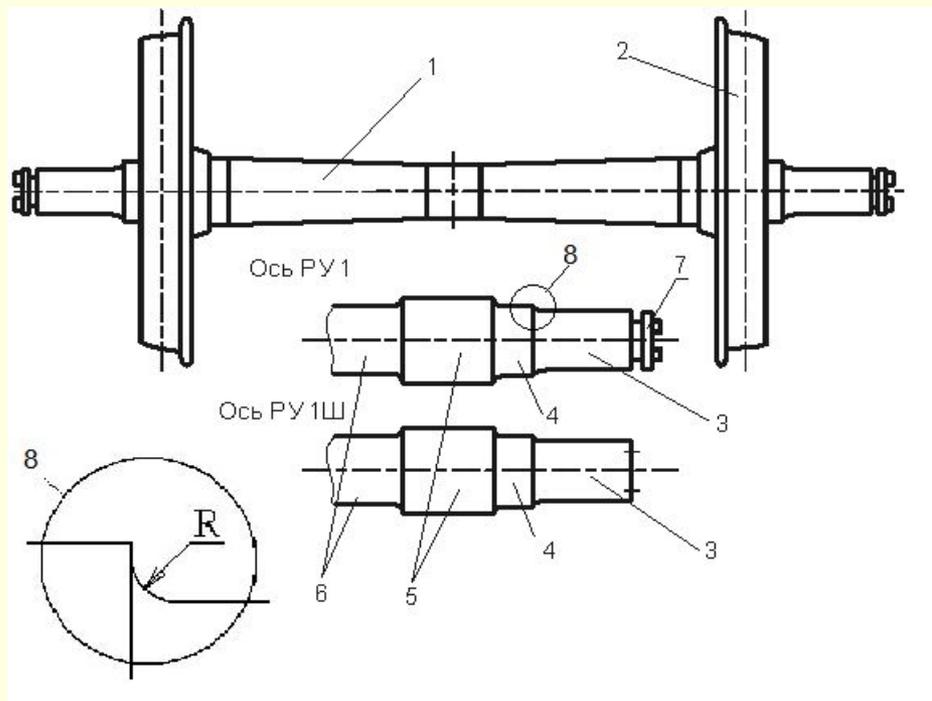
Колесная пара и форма шейки оси: 1 - ось; 2 - колесо;
